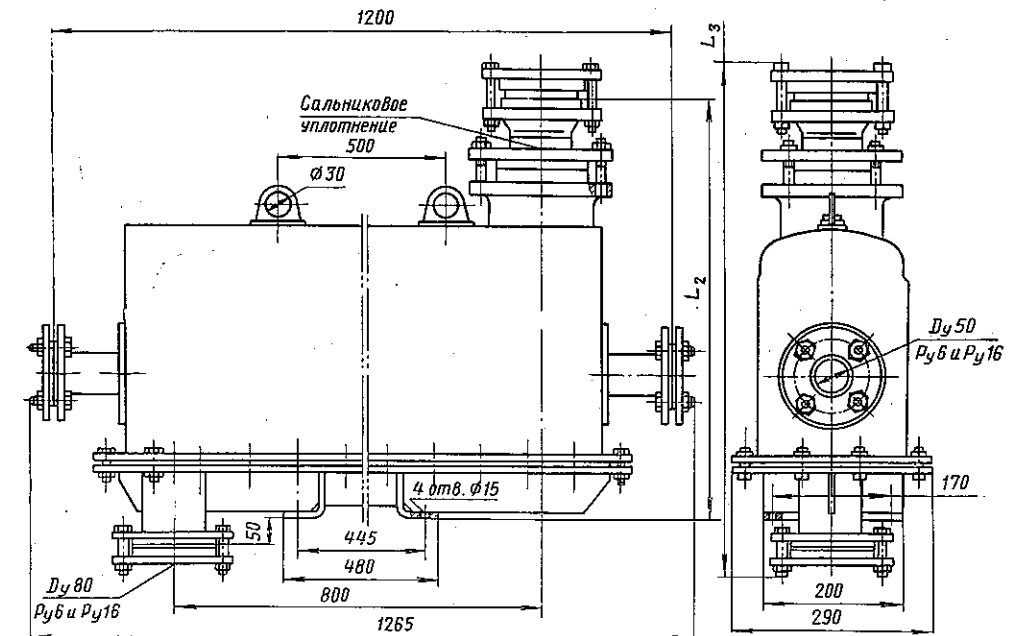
Общий вид теплообменника с габаритными и присоединительными размерами (исполнение II)
